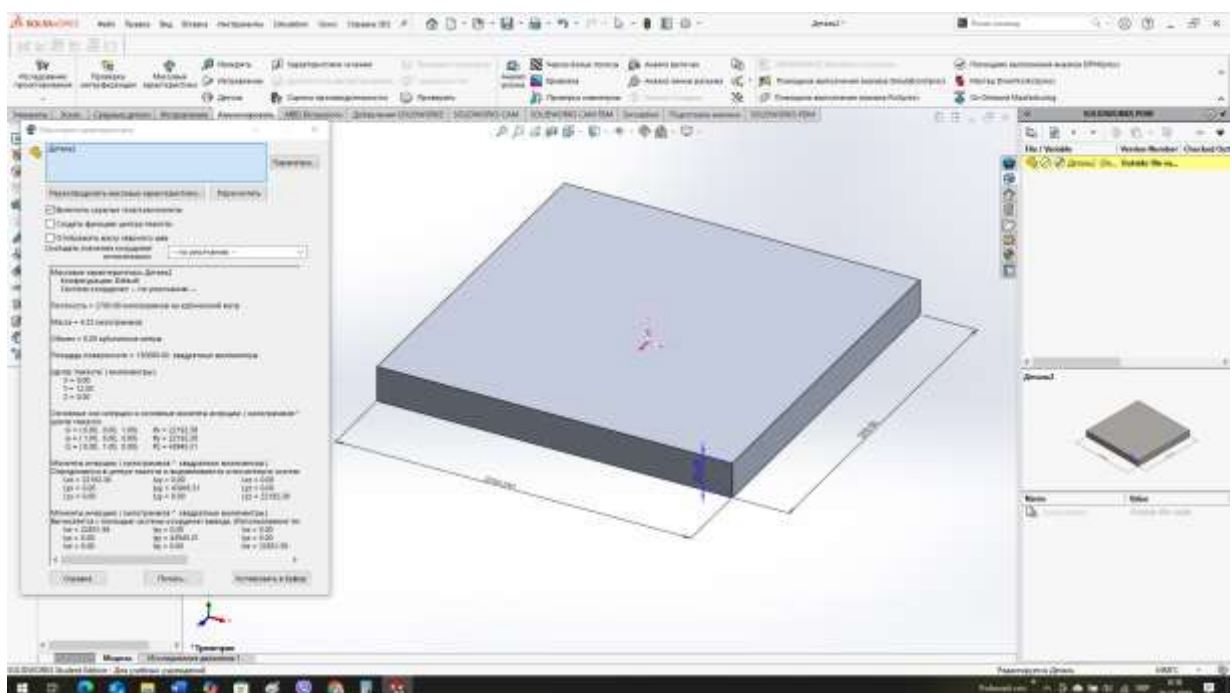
Визначення маси заготовки в середовищі SOLIDWORKS 2025
